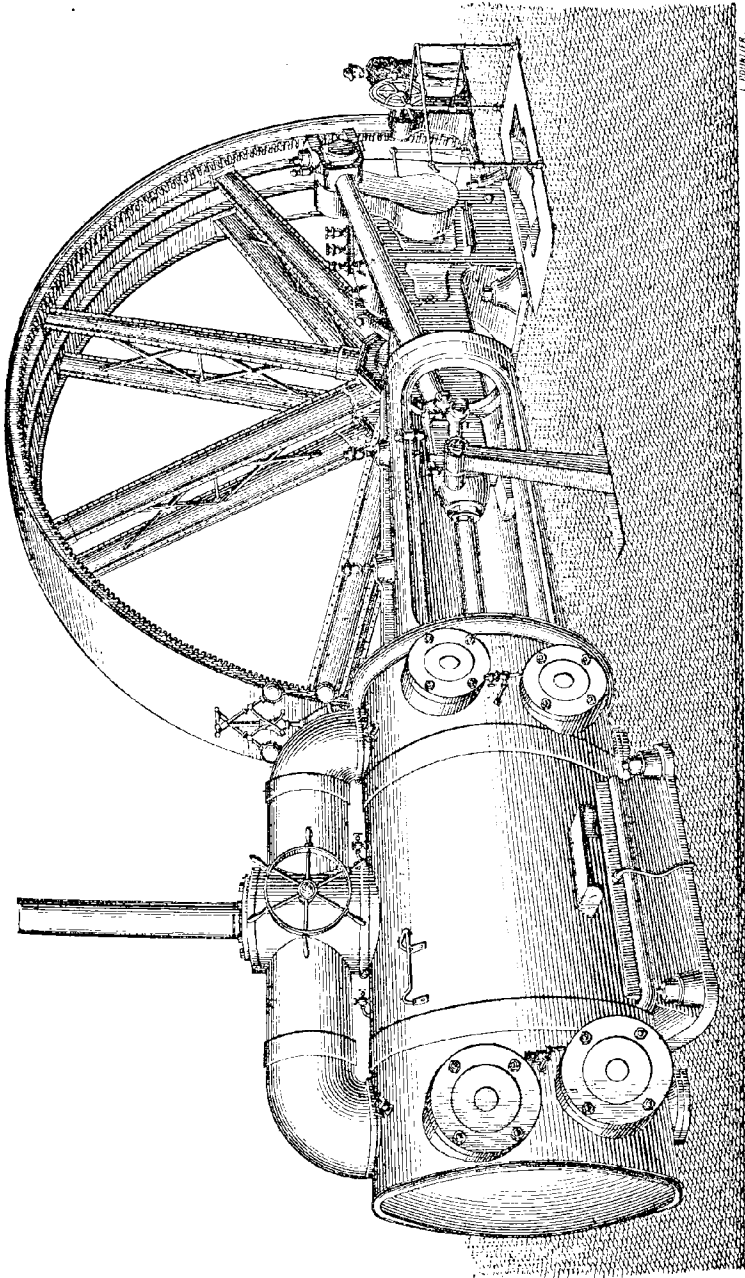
Machine Faircut à quatre tiroirs (vue perspective).
